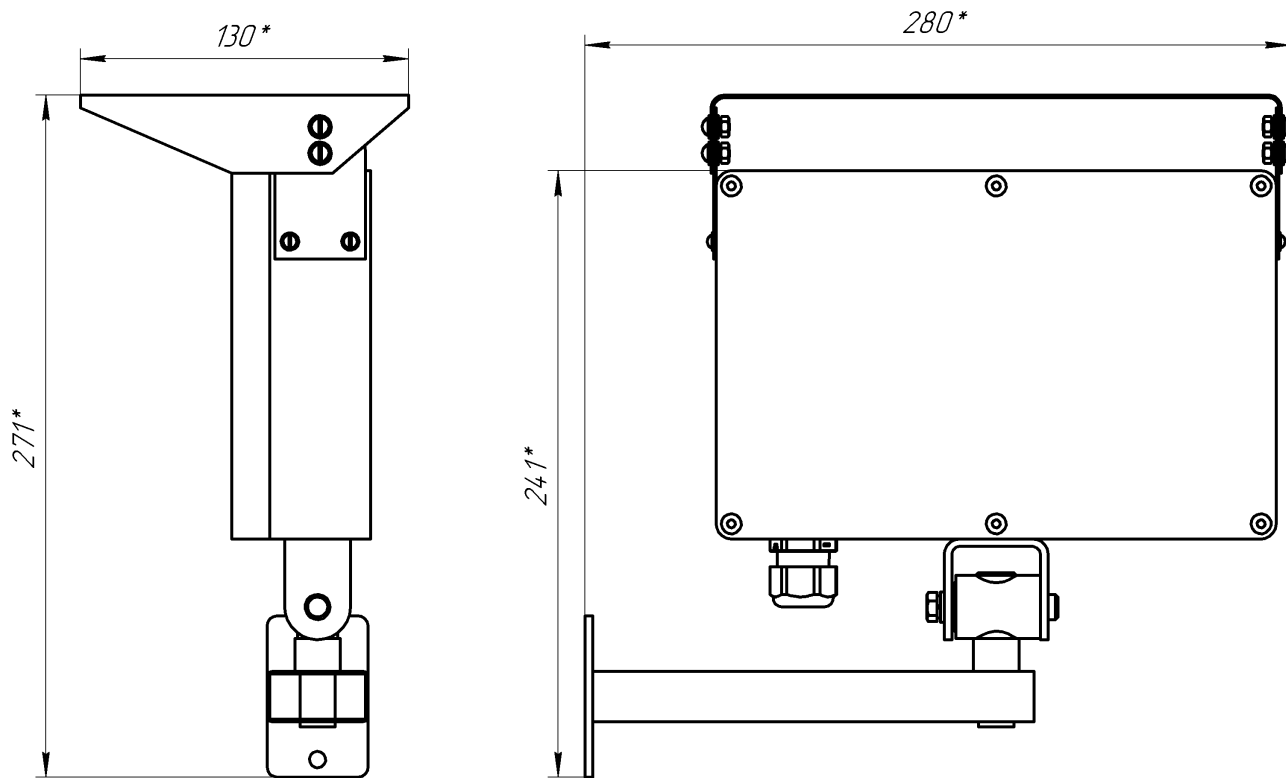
Габаритные размеры извещателя с КМ1.
